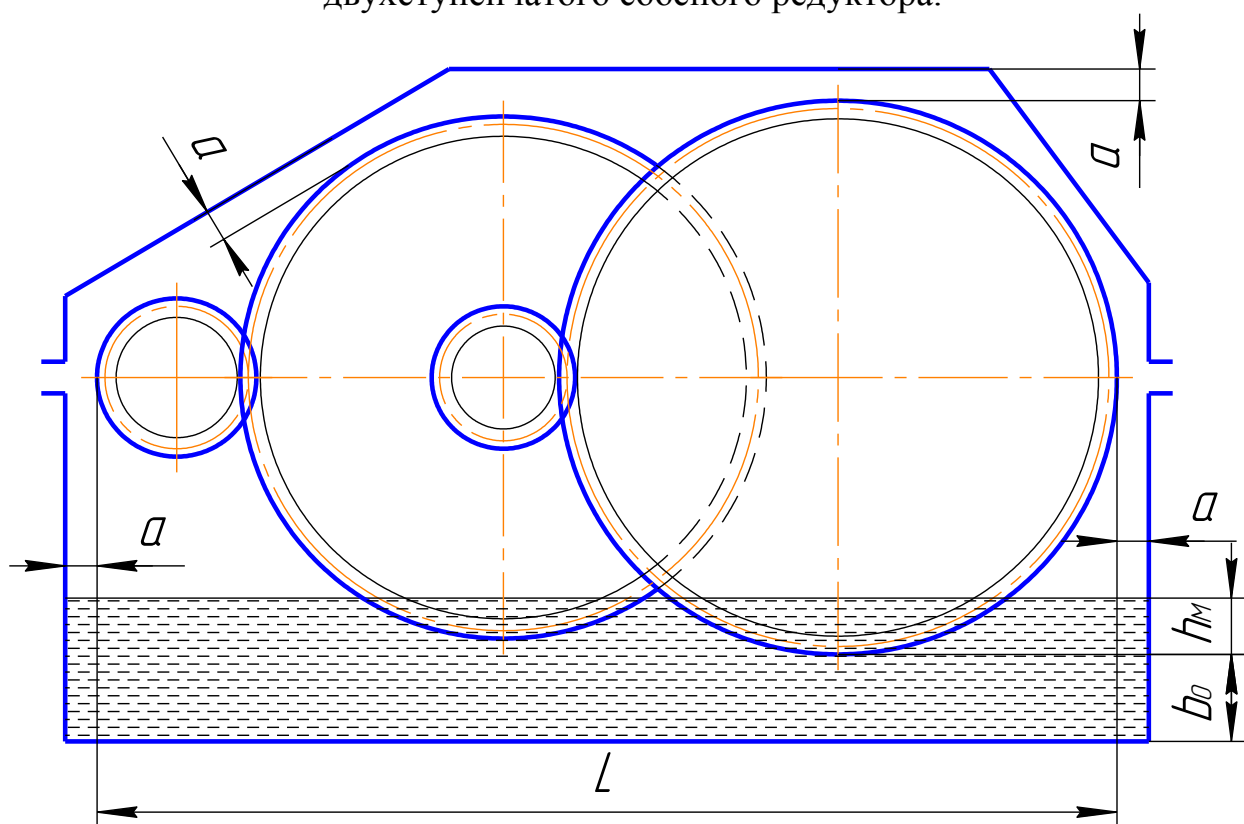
Компонка цилиндрического двухступенчатого редуктора развернутой схемы.
